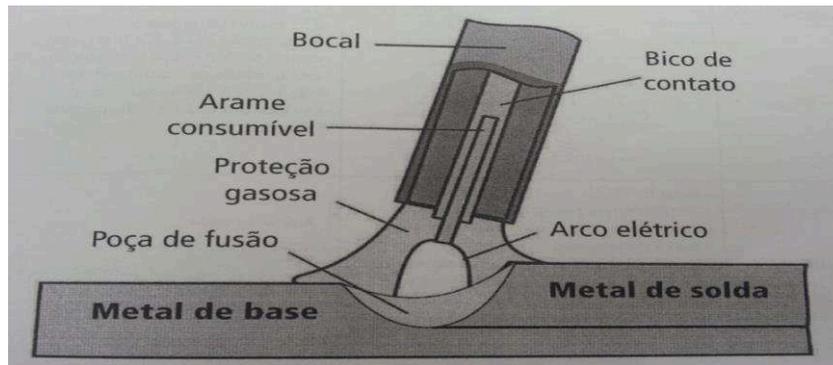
Processo MIG/ MAG GMAW (Gas Metal Arc Welding)
